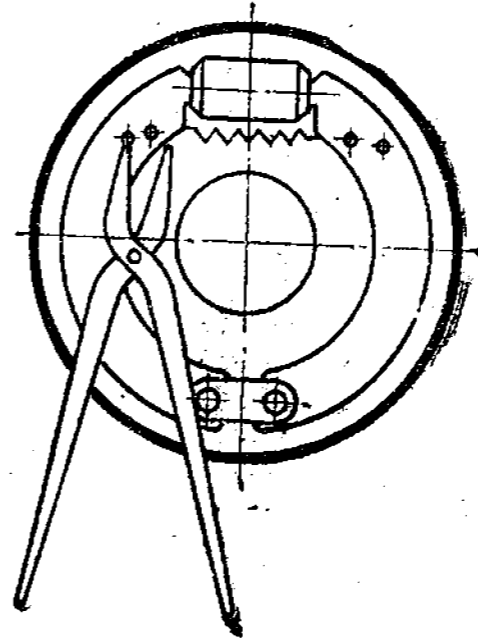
Щипцы для снятия и установки стяжных пружин колодок тормоза
